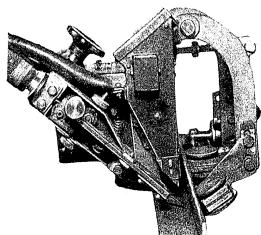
Автоматическая сварочная головка ГСА-1-2 для сварки угловых швов
